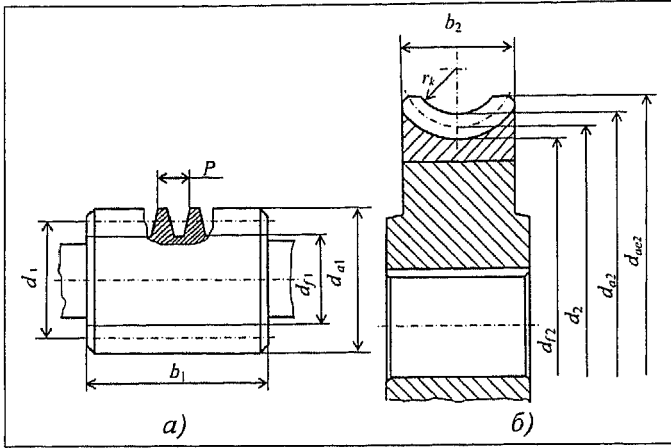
Основные геометрические параметры: а – червяка; б – червячного колеса
